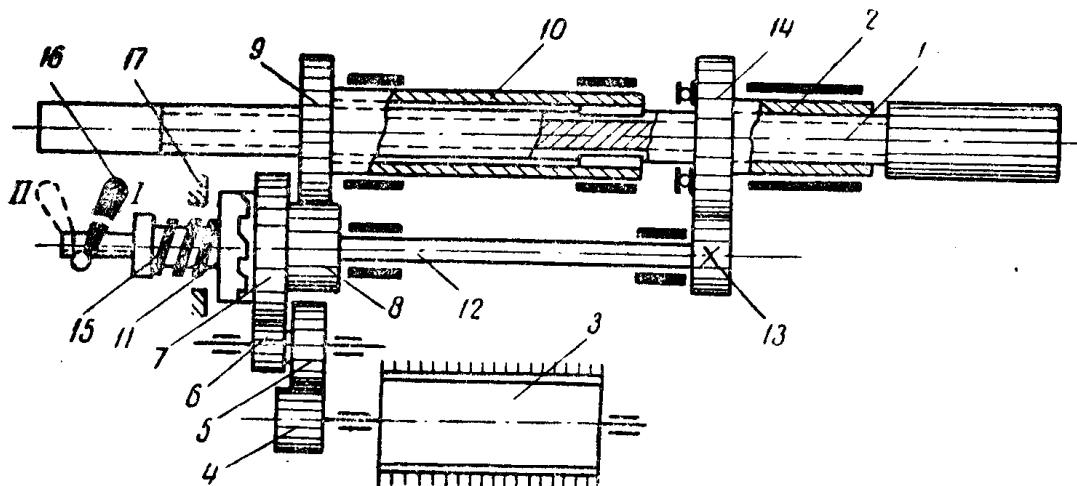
Кинематическая схема сверла ЭБК-2 м:
